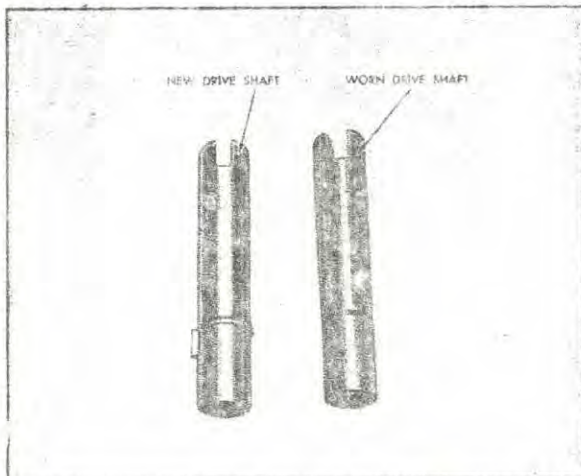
Ejes de impulsión de bomba de engranajes nuevo y gastado.
